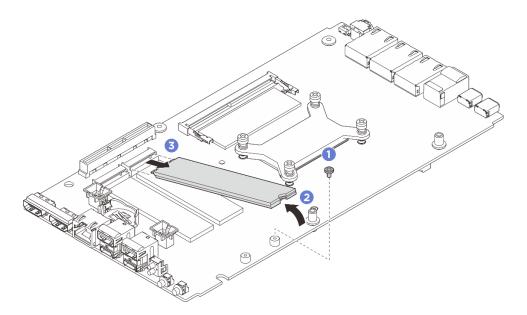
Entfernen des M.2-Laufwerks (Formfaktor 22110)
